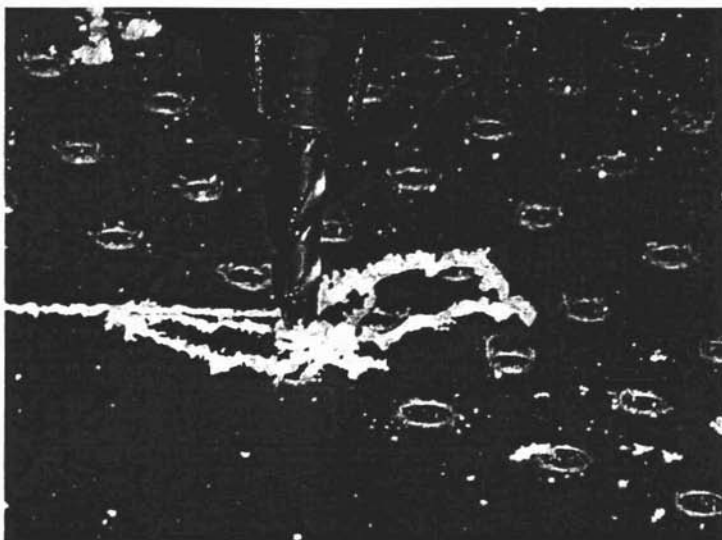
Vista del taladro vertical realizando los barrenos en los paneles transversales
